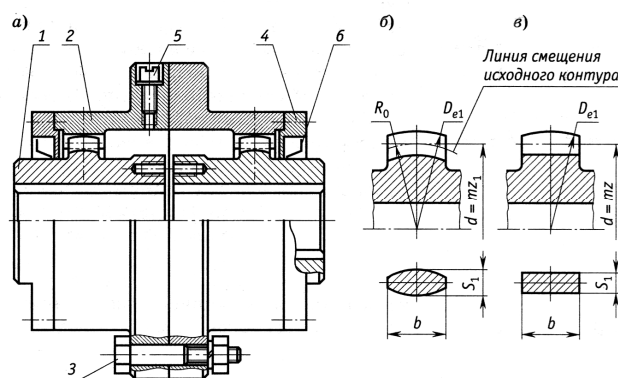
Зубчатая муфты (а) и профиль зубьев бочкообразный (б) и прямой (в)
